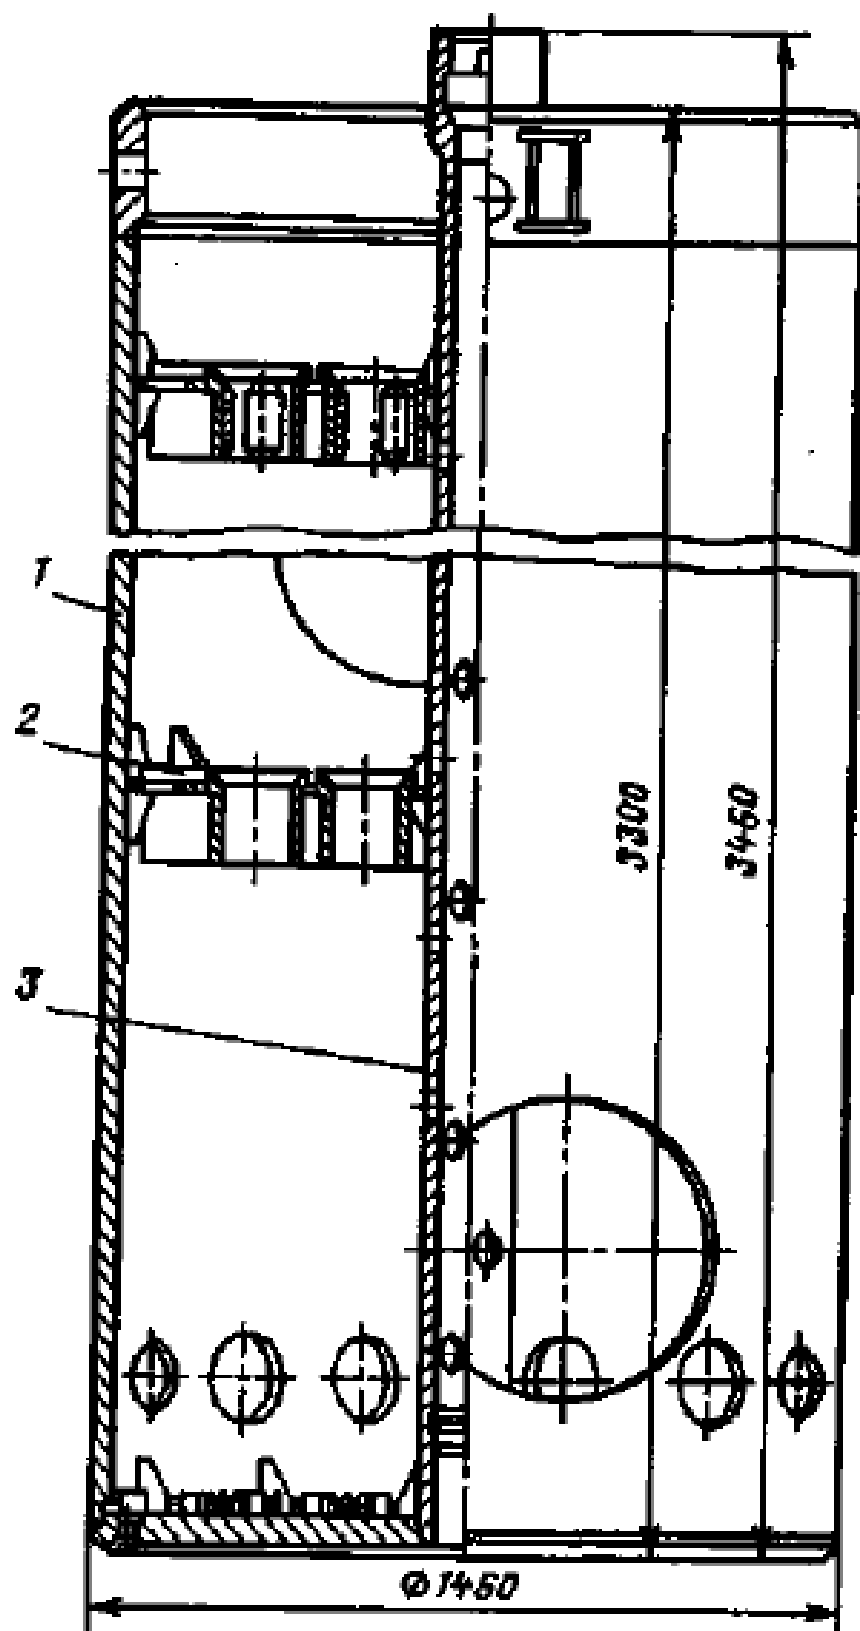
Чехол транспортного упаковочного комплекта для отработавшего топлива реактора ВВЭР-440: 1 – обечайка; 2 – решетка; 3 – центральная труба под захват
